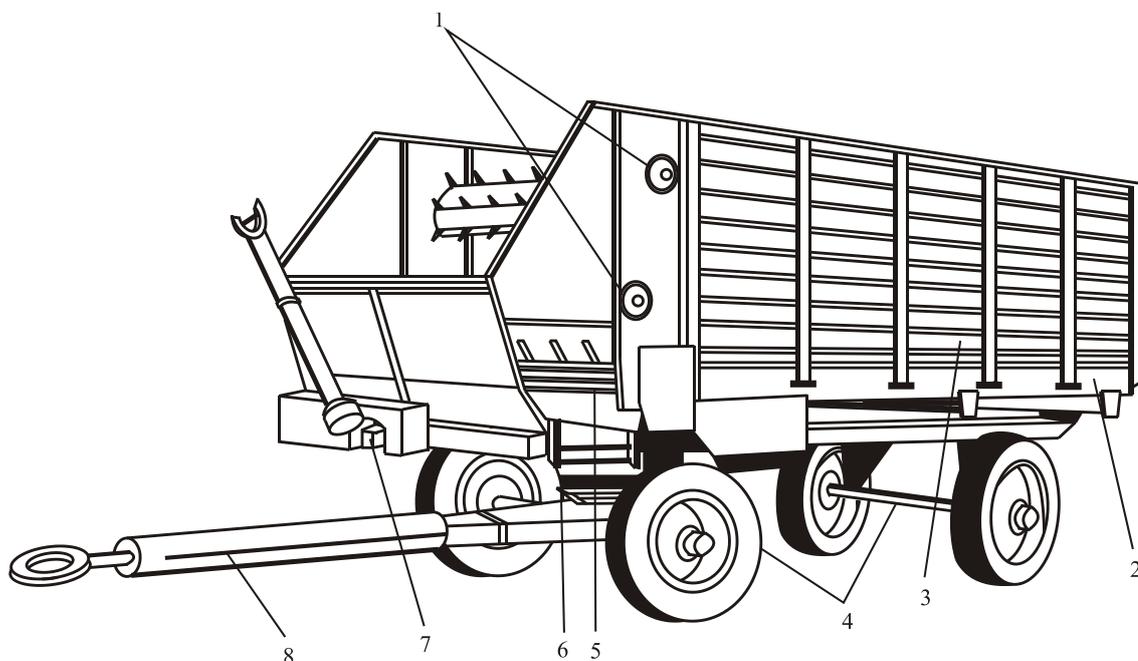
Кормораздатчик тракторный универсальный КТУ-10А:
